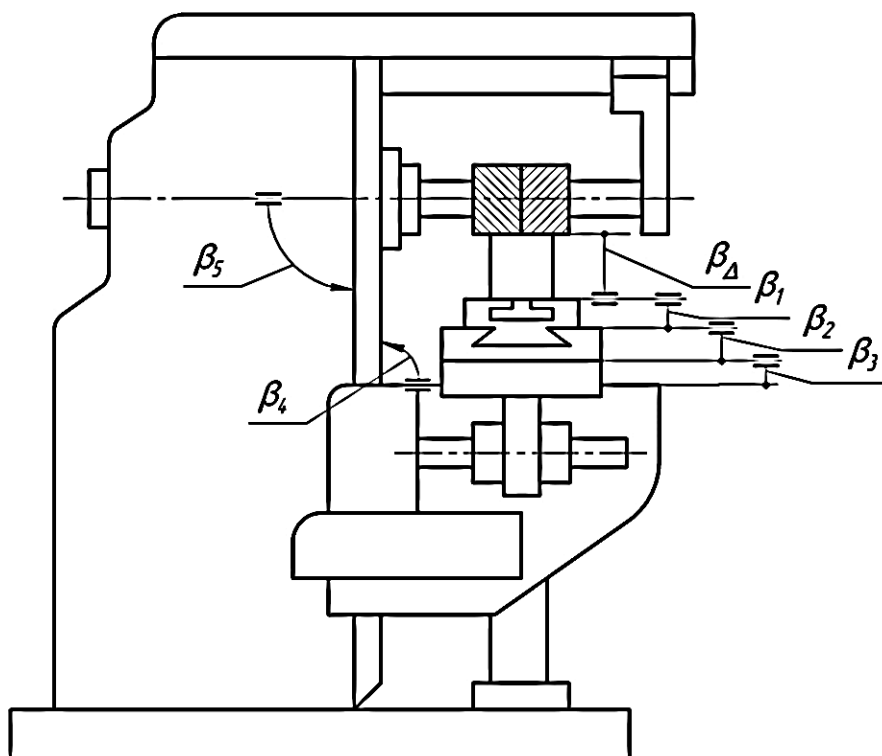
Схема технологічного розмірного ланцюга фрезерного верстата
